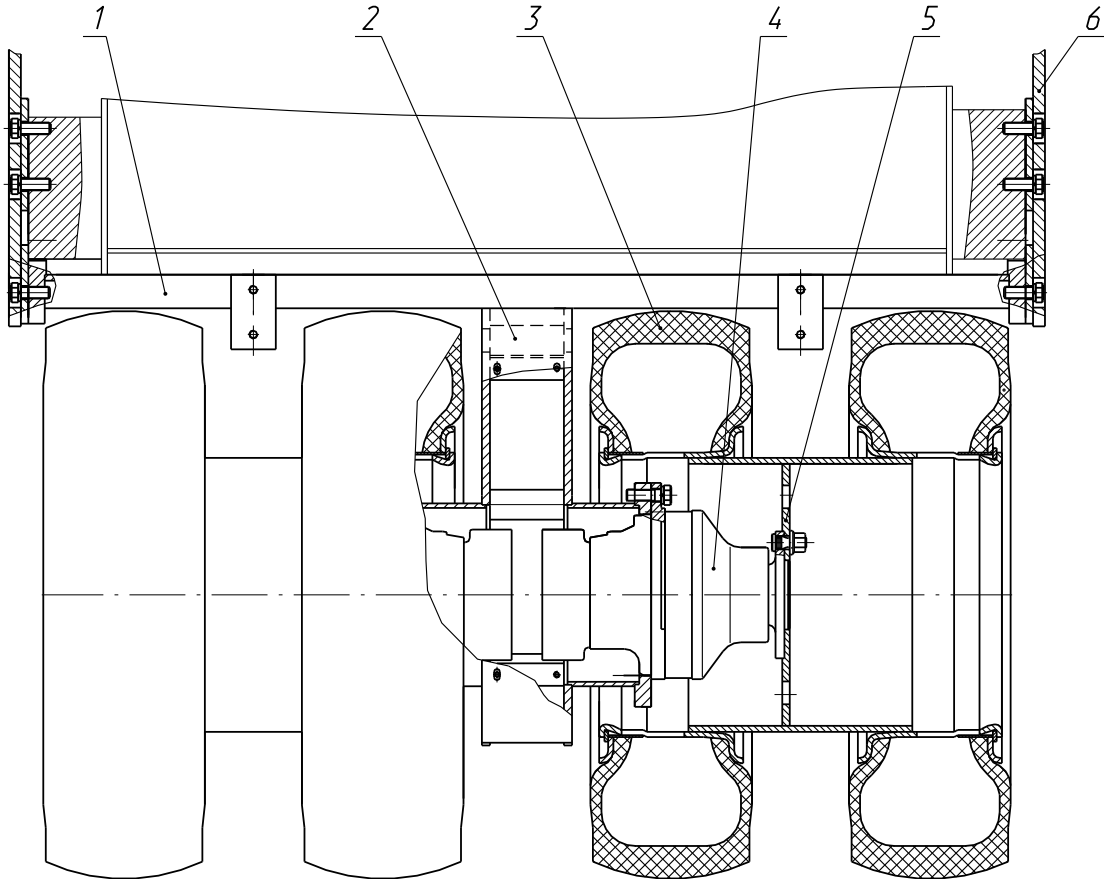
Схема расположения пробок для слива масла из мотор - редуктора и контроля уровня масла в мотор - редукторе
